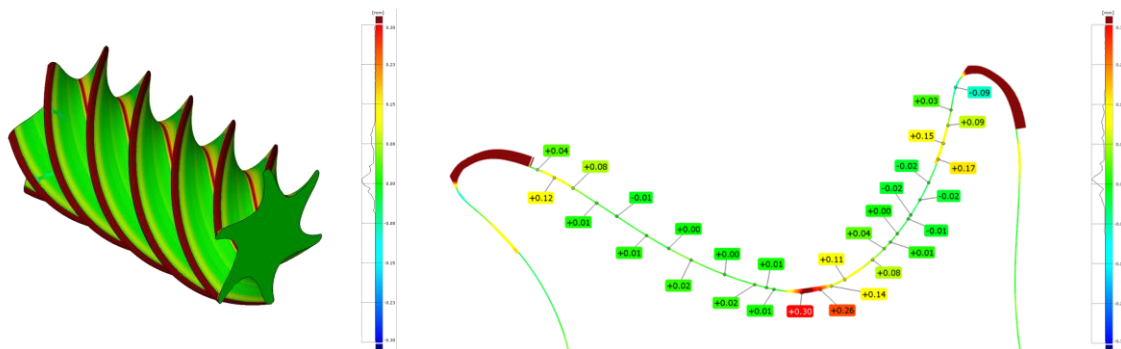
Desviación dimensional teórica del compresor de tornillo sin fin hembra no simétrico mediante dos herramientas de forma.
